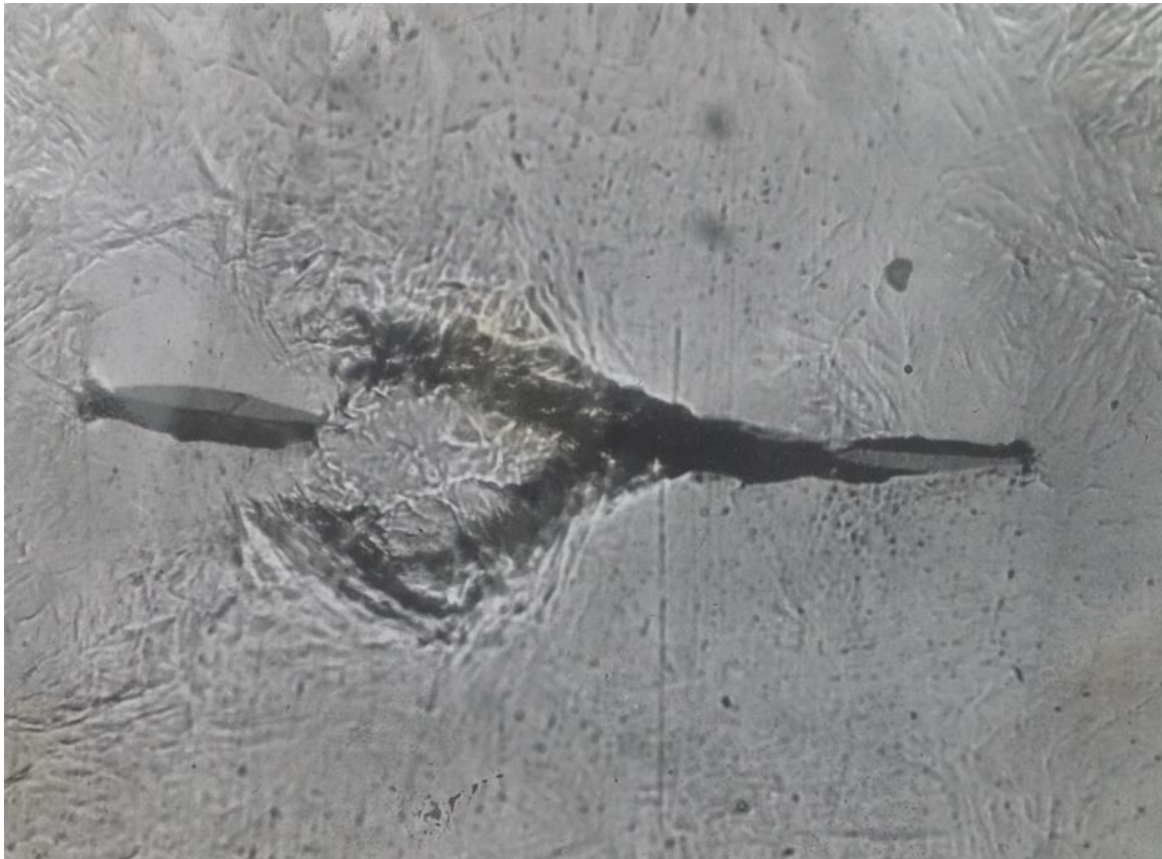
Осьові розшарування в квадратній заготівлі киплячої сталі
